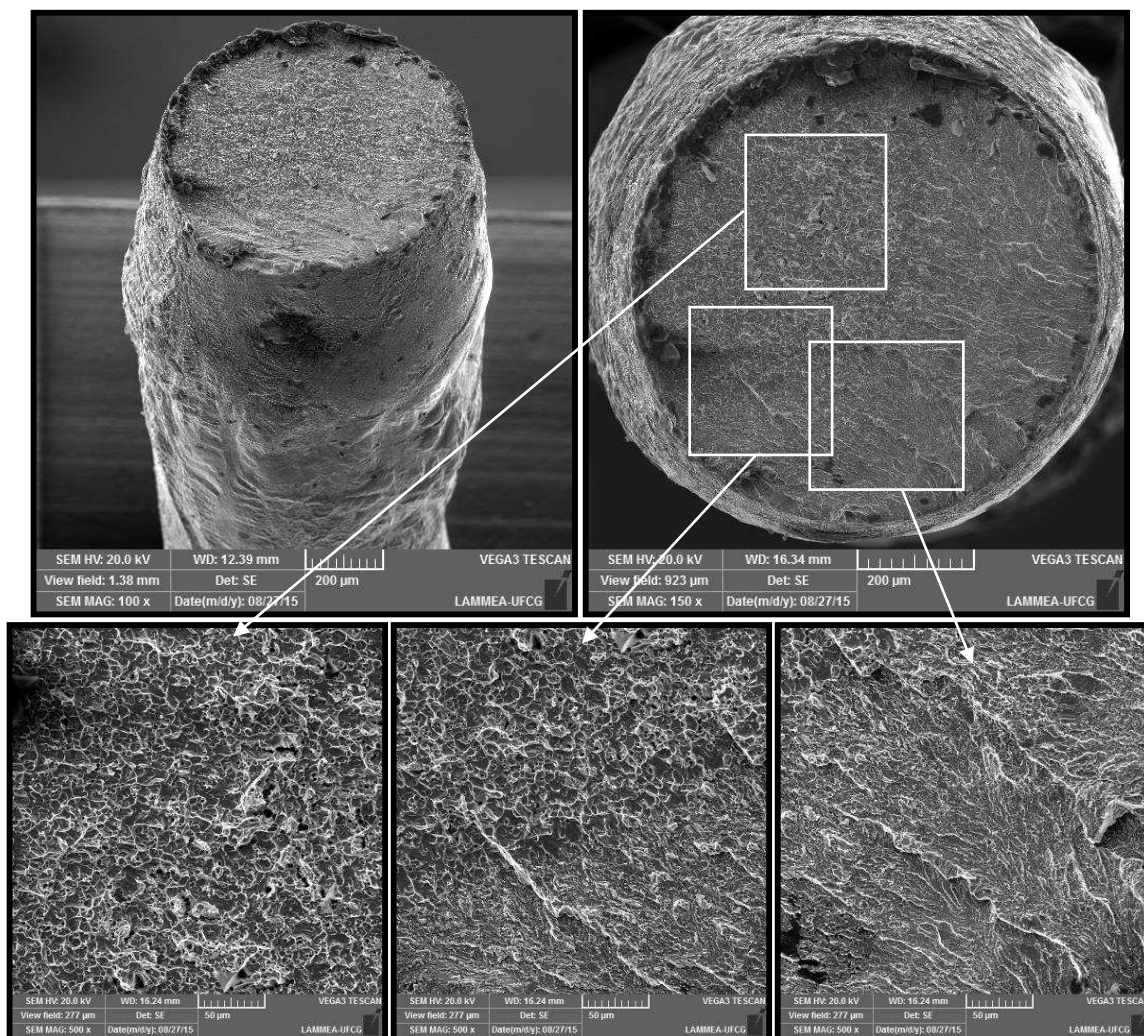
Superfície de fratura do fio atuador soldado na configuração 9ms/60% e testado a 90°C.
